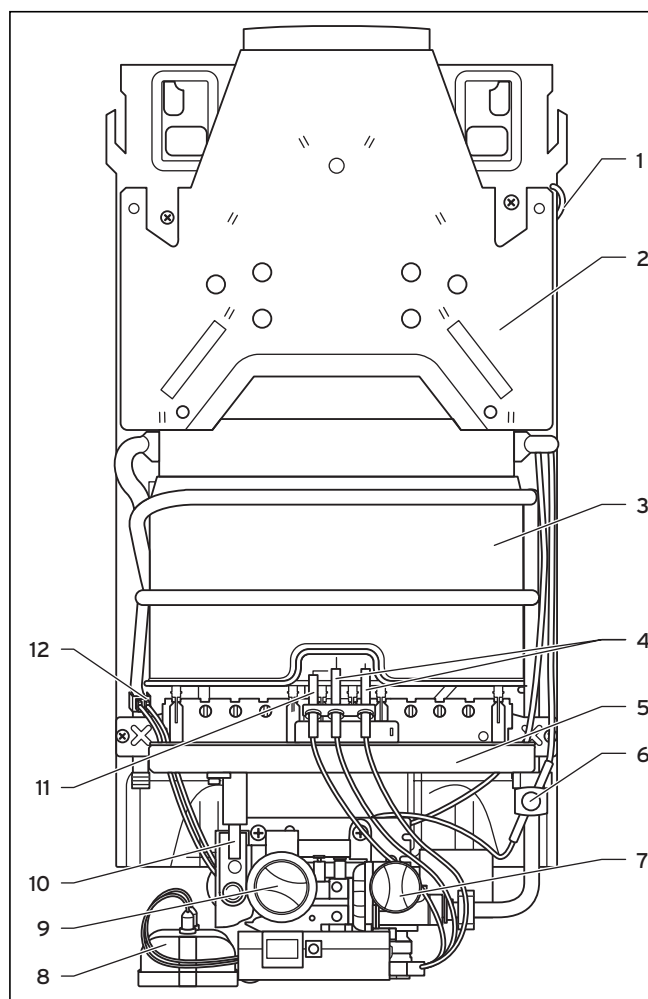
Grupos constructivos 14-0/0 del aparato LCD, tipo XI
